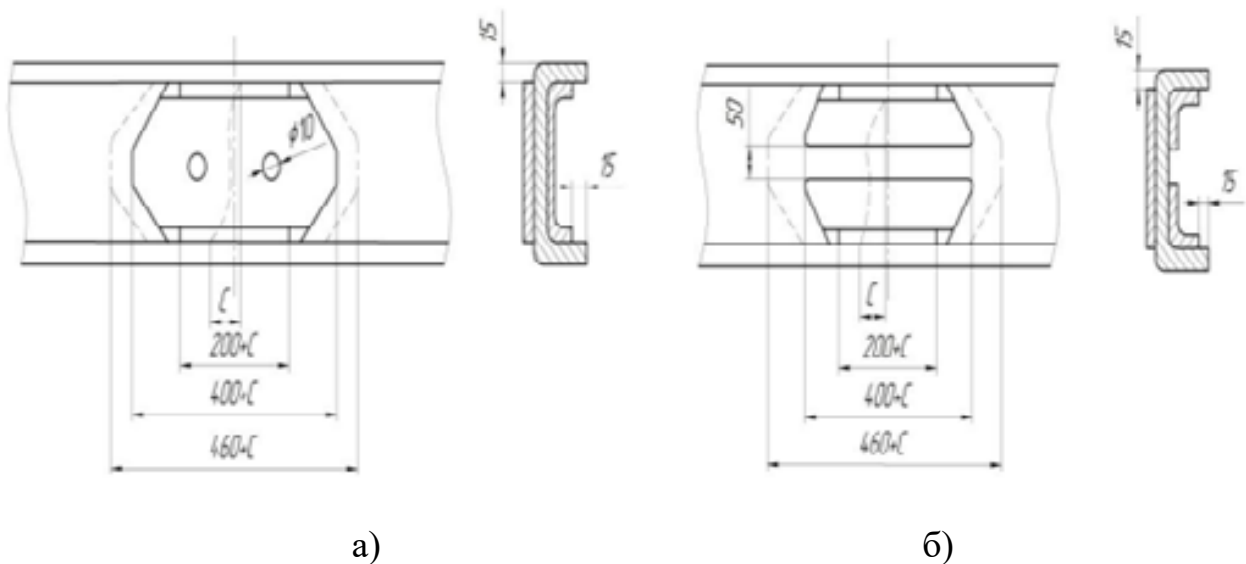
Конструктивне підсилення під час зварюванні переломів або зварного з'єднання швелерів встик
